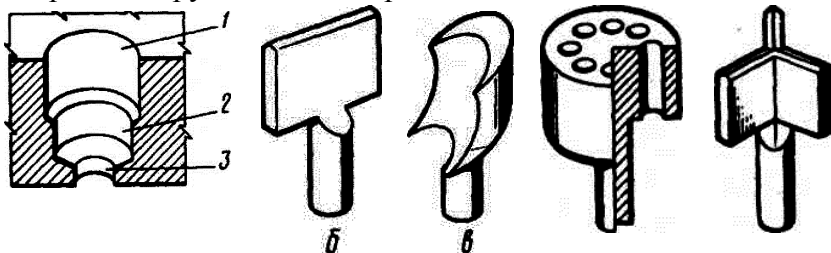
Формуючі елементи матриць із вкладишами: а - профіль формуючого каналу: 1 - верхня зона; 2 - перехідна зона; 3 - формуюча щілина; б, в, г, д - двохопорний, серпоподібний, циліндричний і трьохпорний вкладиші
